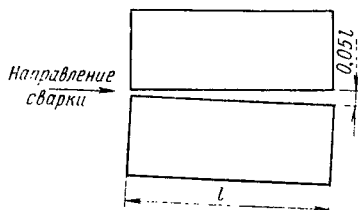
Разведение кромок при сварке без прихватов
